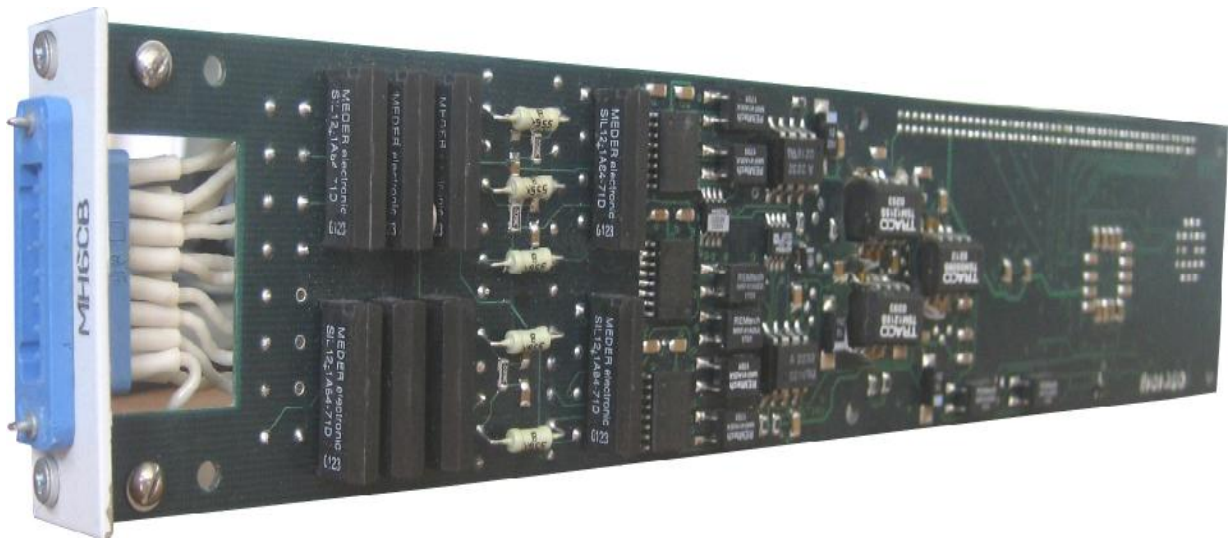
Внешний вид измерителя МН6СВ ФТКС.468266.003
